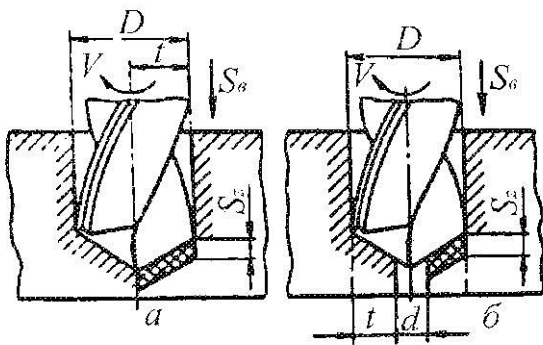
Схеми свердління (а) і розсвердлювання (б)
